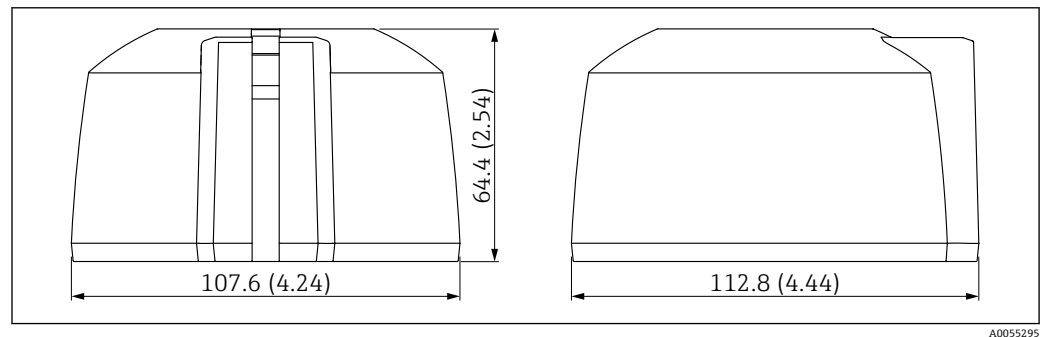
G1/NPT1 防护罩的外形尺寸（顶部电缆入口）。测量单位 mm (in)
